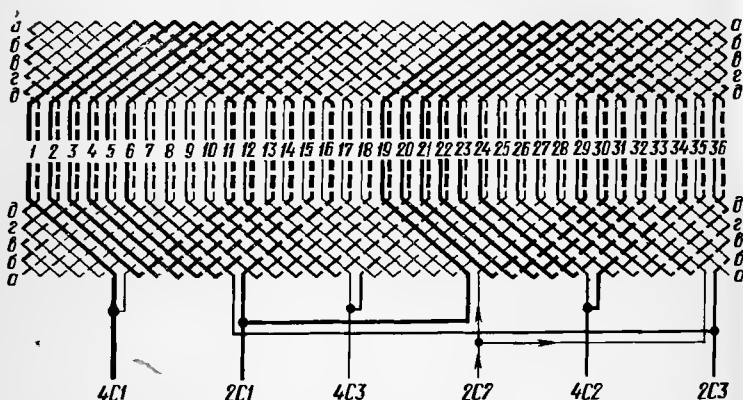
Развернутая схема двухскоростной обмотки статора.
